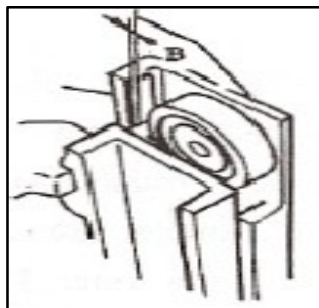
32 Tolerancia de mástil-Rodamiento
